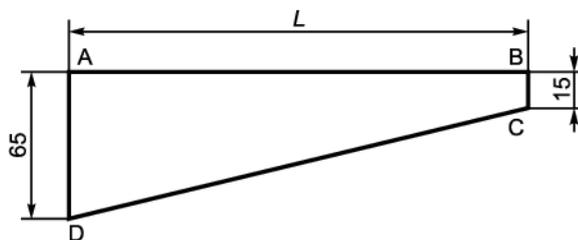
Образец для испытаний типа 2 (клиновидный)
